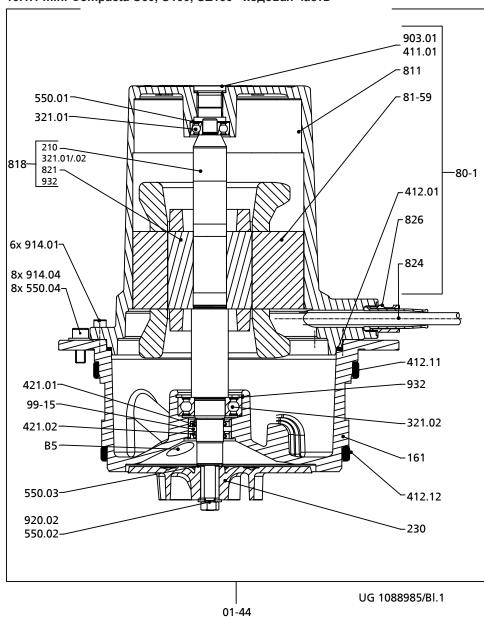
Сборочный чертеж mini-Compacta U60, U100, UZ150 — рабочая часть
